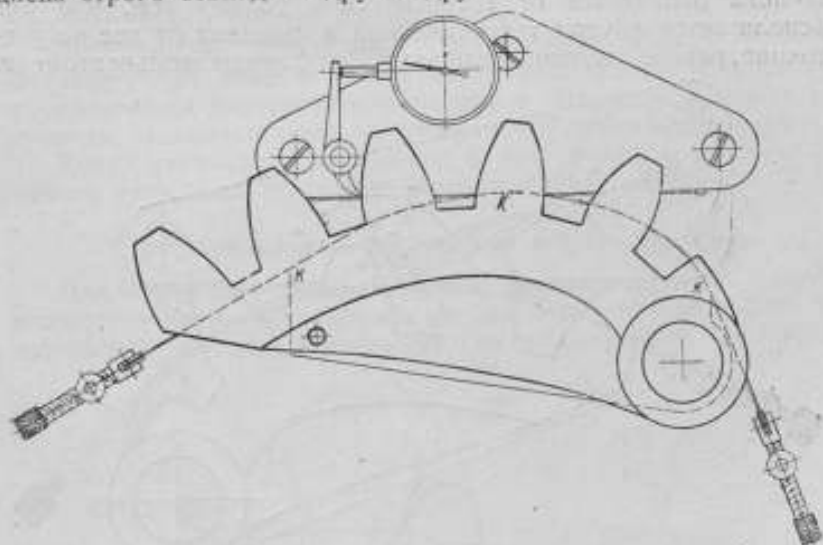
Схема первого типа эвольвентомера для проверки зубцов некруглого колеса.
